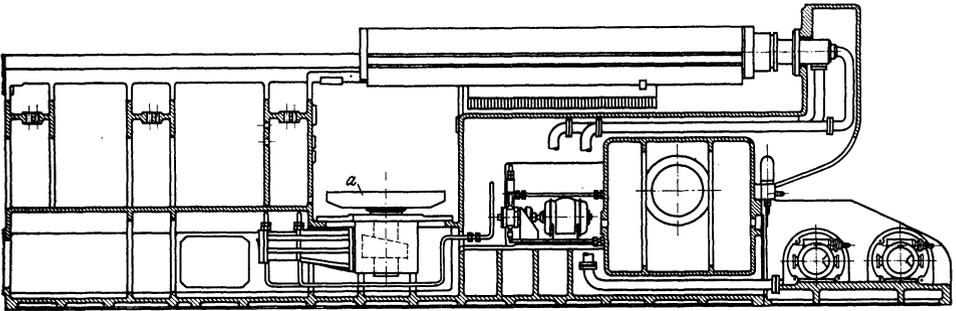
Waagerechte Sonderräummaschine für Zylinderblockbearbeitung.
